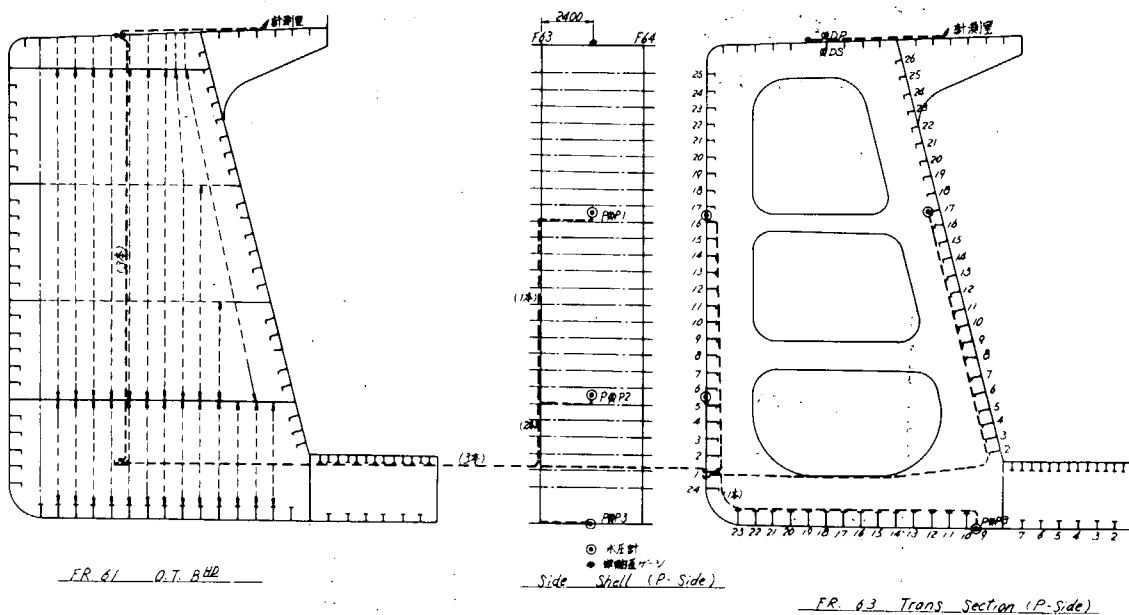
6 3 1/2 SECTION 水圧計配置図 (P-Side)
